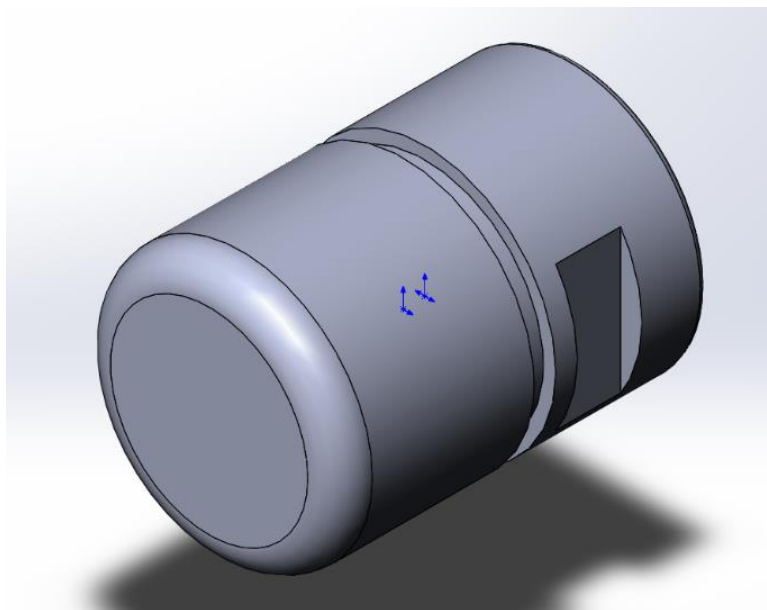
цилиндр соединен с прокладкой и цилиндром с вырезом под ключ
